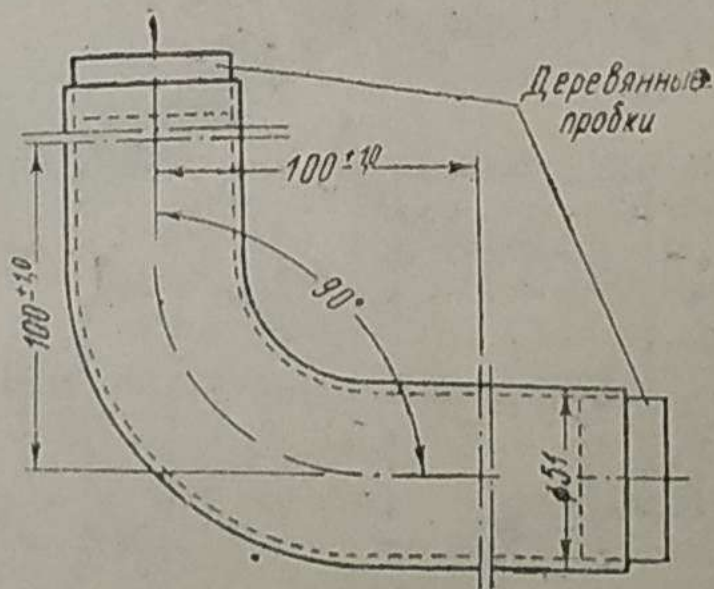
Патрубок, изготовленный на Бавленском заводе.
